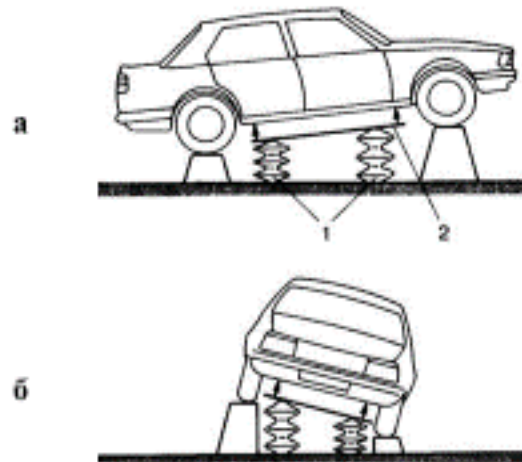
Установка автомобиля на измерительный стенд с пневматическим приспособом для контроля основы кузова в продольном (а) и поперечном (б) направлениях
